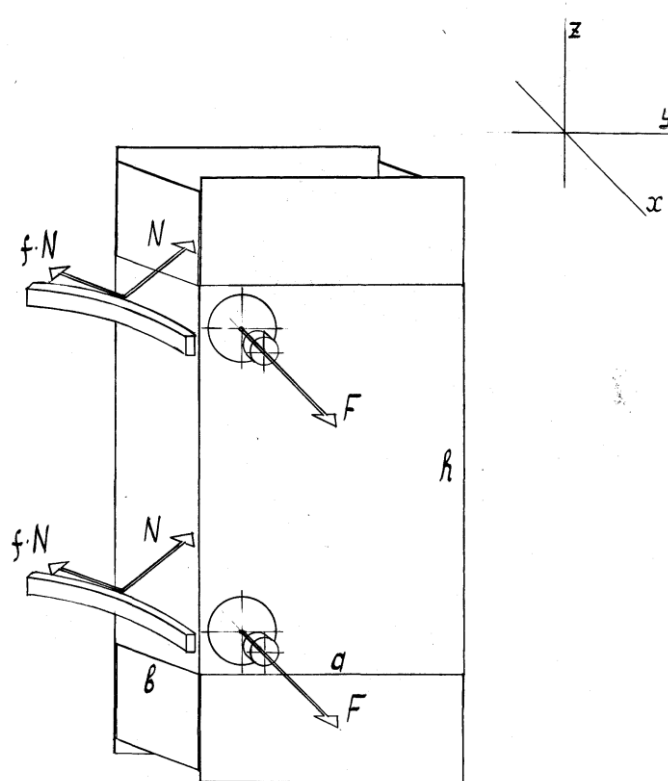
Схема розгортання плоско-складеної заготовки за допомогою вакуум-захватів.
